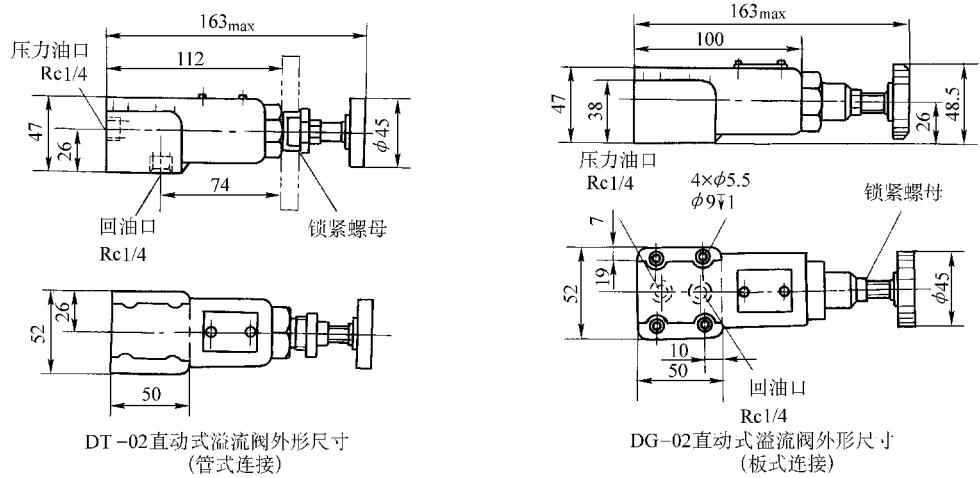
D 型遥控溢流阀、直动式溢流阀外形尺寸 (续)
